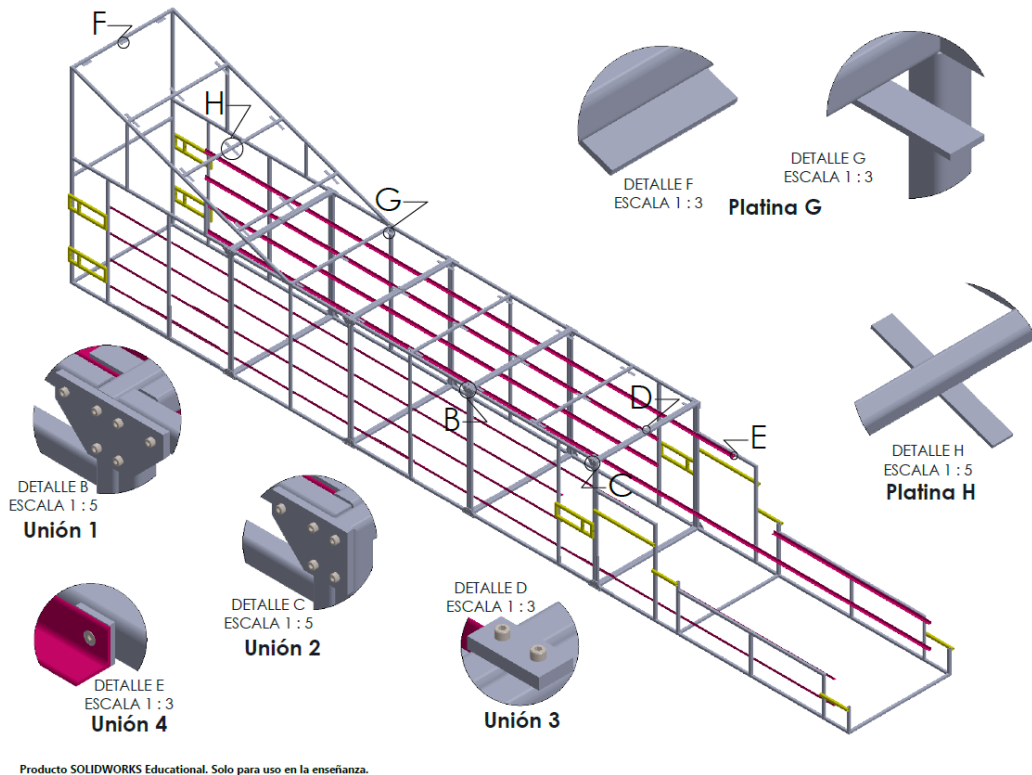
Medidas de las platinas para los paneles de cerramiento
